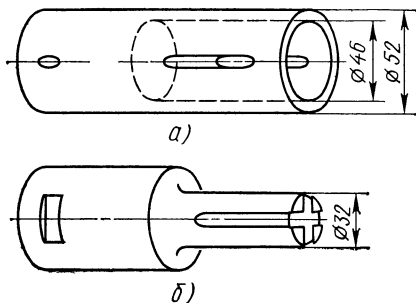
Инструменты для обработки отверстий большого диаметра:
